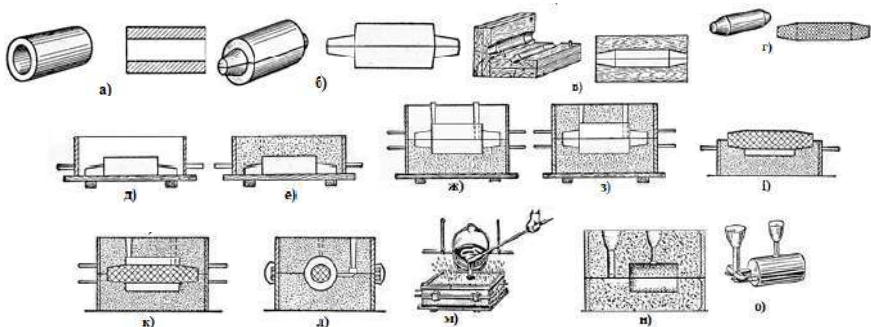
Послідовність виготовлення ливарної форми
